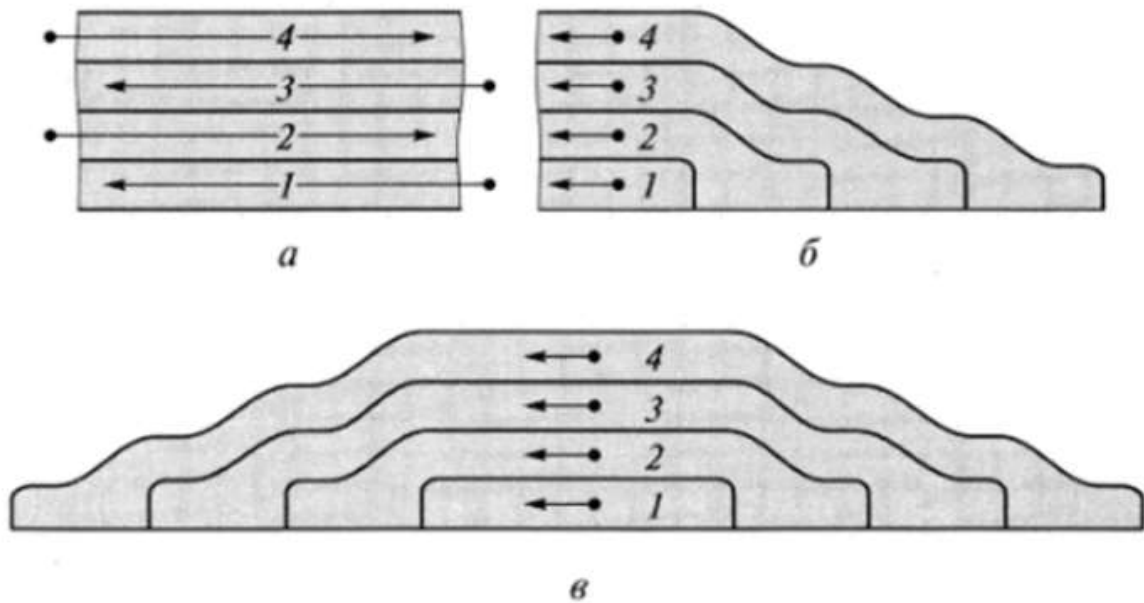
Схеми виконання багатошарового зварювання
